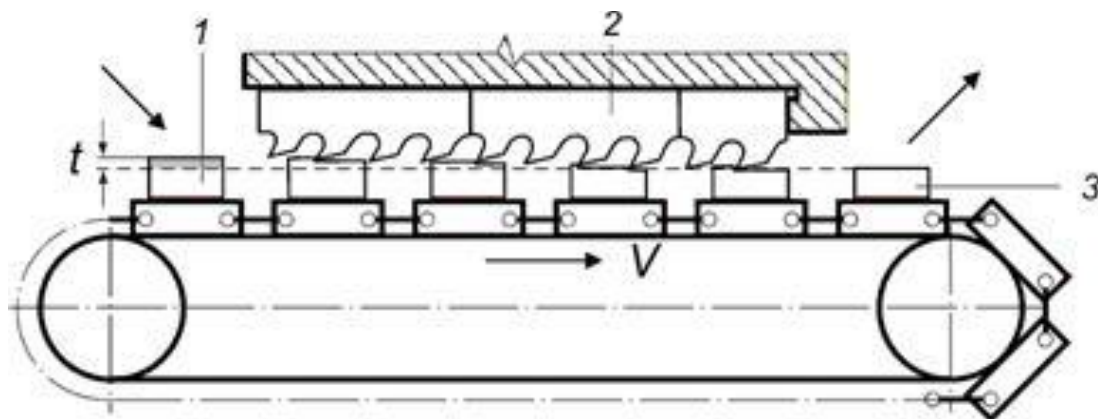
Схема непрерывного протягивания на горизонтально-протяжном станке конвейерного типа
